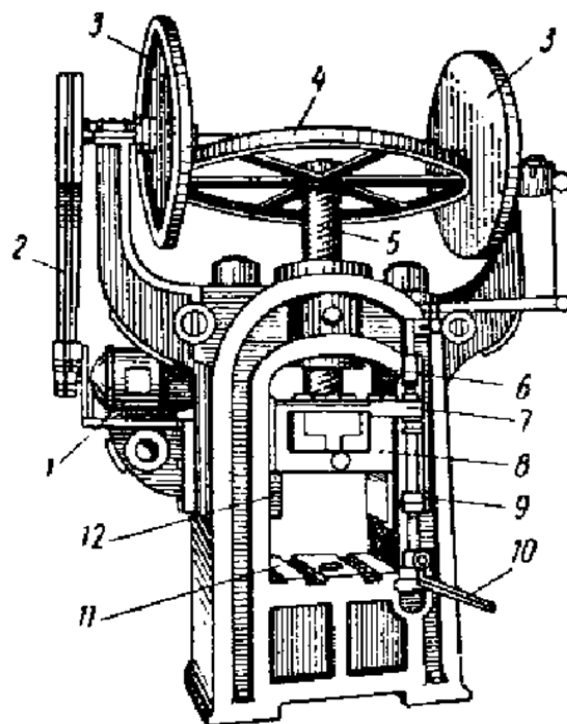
Винтовой фрикционный пресс: 1 – электродвигатель; 2 – ременная передача; 3 – фрикционные диски; 4 – маховик; 5 – винтовой шпиндель; 6 – неподвижно-закрепленная гайка; 7 – специальный выступ; 8 – ползун; 9 – кулачок; 10 – рукоятка управления; 11 – стол; 12 – направляющие.
